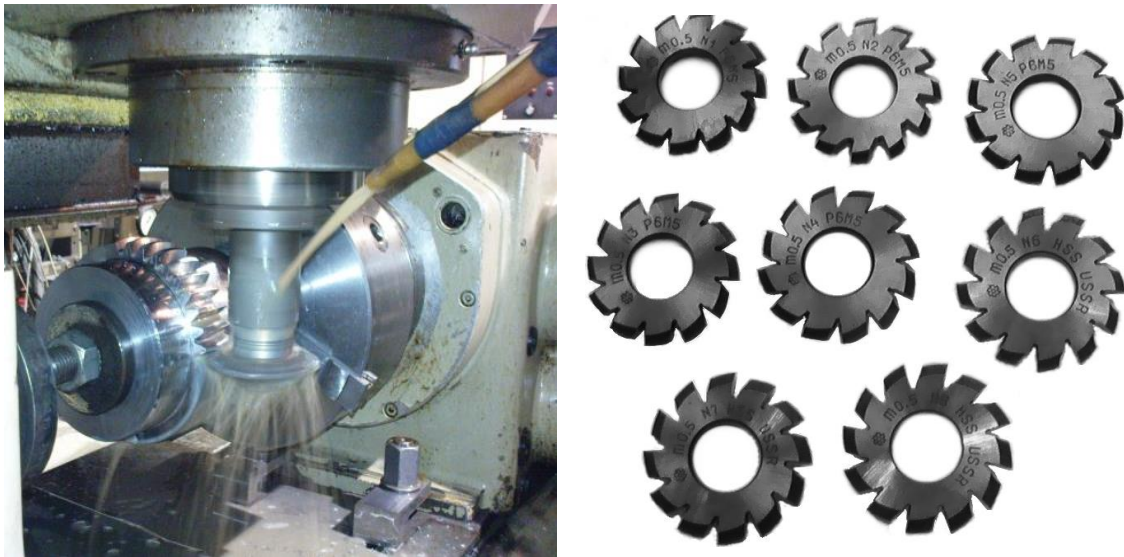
Обробка зубчастих коліс дисковими фрезами на вертикально-фрезерному верстаті
